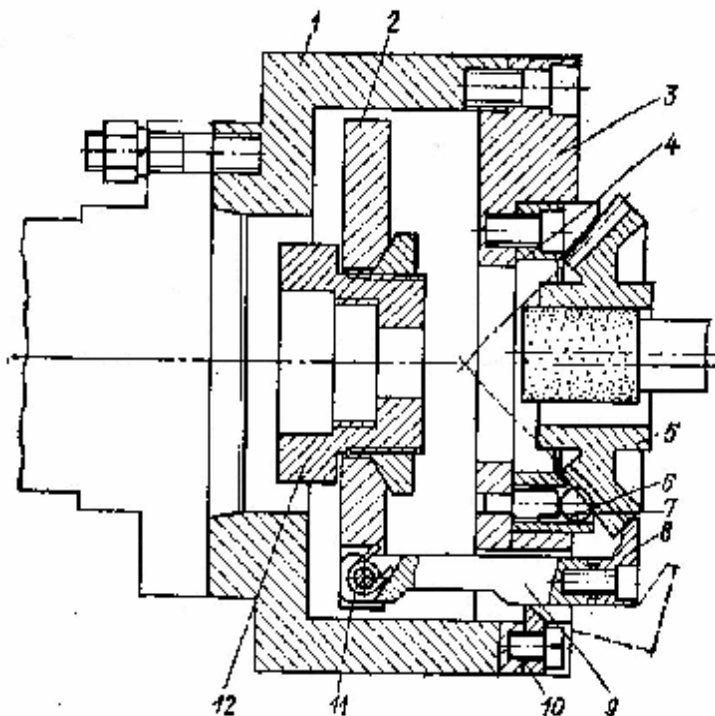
Рычажный патрон для крепления конической шестерни
